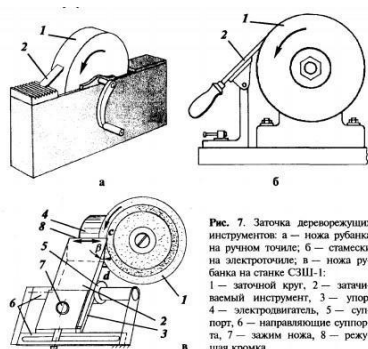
Заточка дереворежущих инструментов: а — нож рубанка на ручном точиле; б — стамески на электроточиле; в — нож рубанка на станке СШН-1: 1 — шлифовальный круг; 2 — заточиваемый инструмент; 3 — упор; 4 — электродвигатель; 5 — суппорт; 6 — направляющие суппорта; 7 — зажим ножа; 8 — режущая кромка
